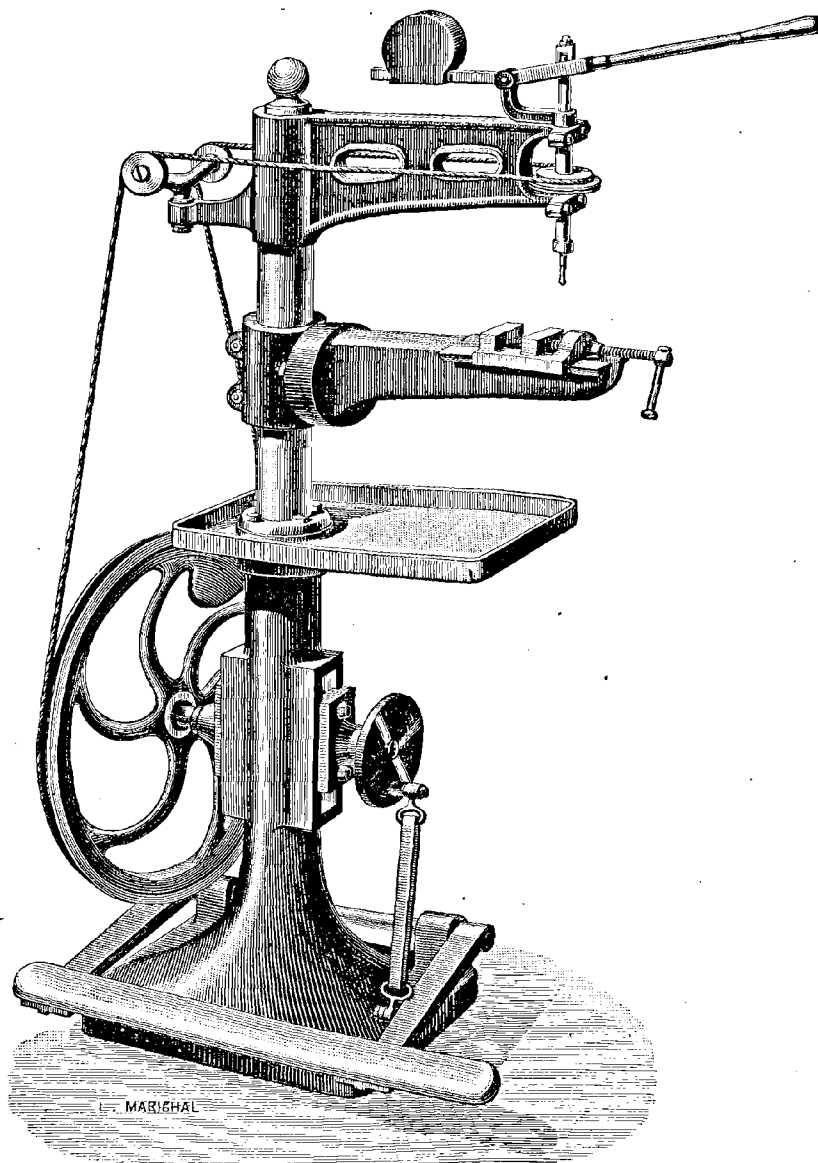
Machine à percer à pédale, bâti en forme de colonne.
